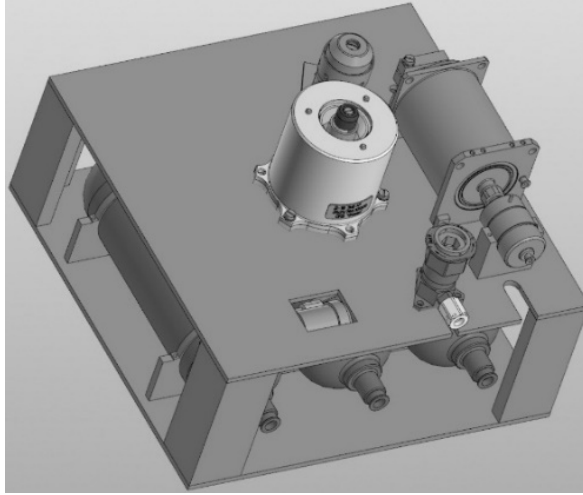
Компоновка двигательной установки КА на базе двигателя Д-18
